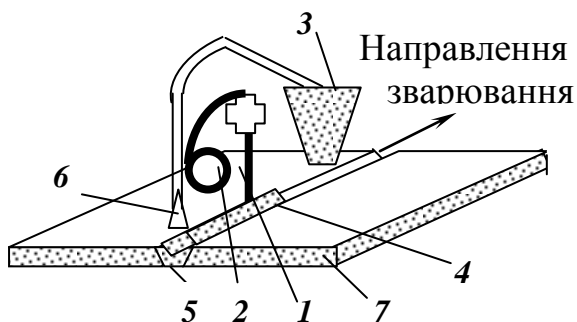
Схема автоматичного електродугового зварювання.
